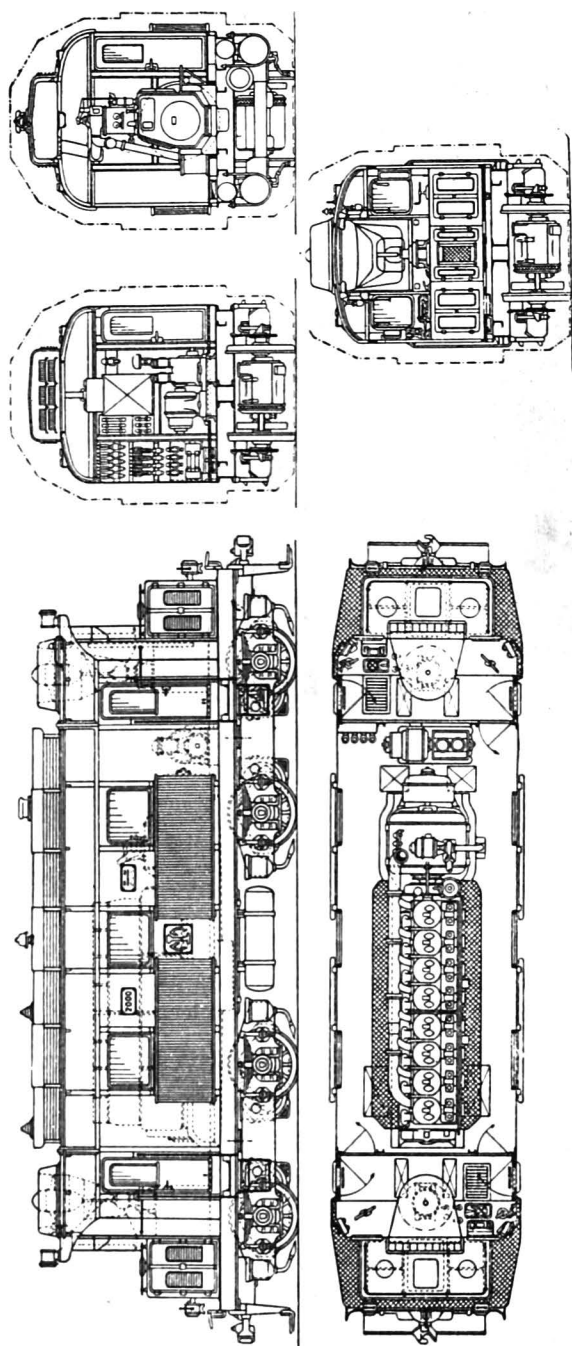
Locomotivă Diesel-electrică 750 C. P.
